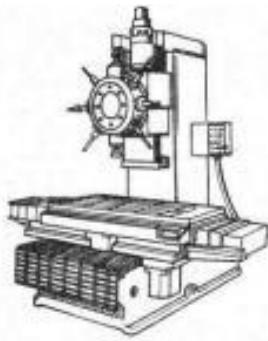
Схема устройства смены шпиндельного узла в виде револьверной головки
